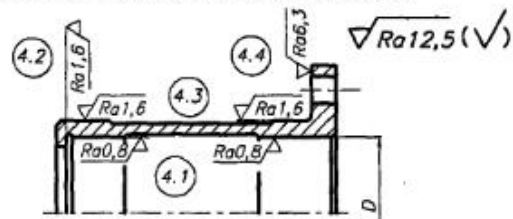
Рекомендуемая шероховатость поверхностей
